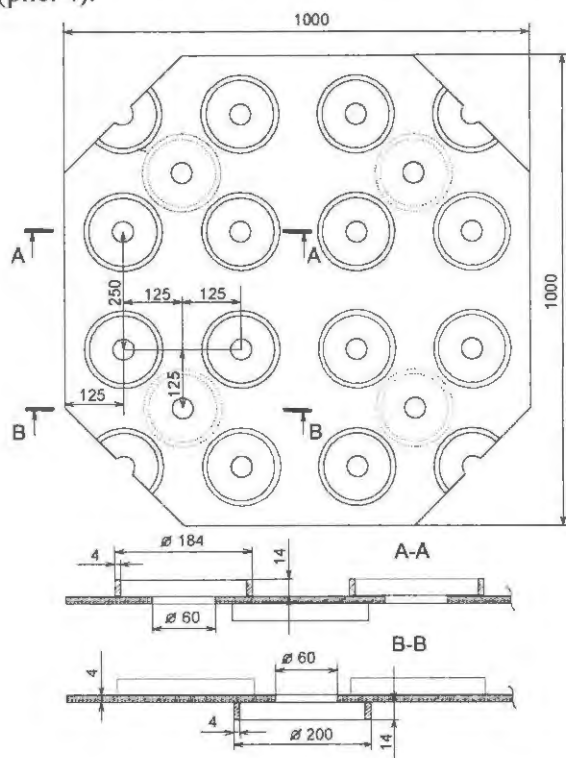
Конструктивная схема опорной конструкции ВО; размеры даны в мм
